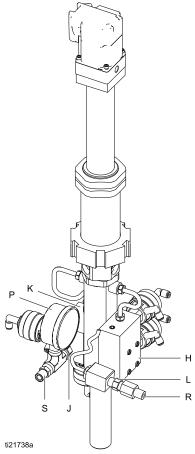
Pumpeneinlass- und -auslassanschlüsse
